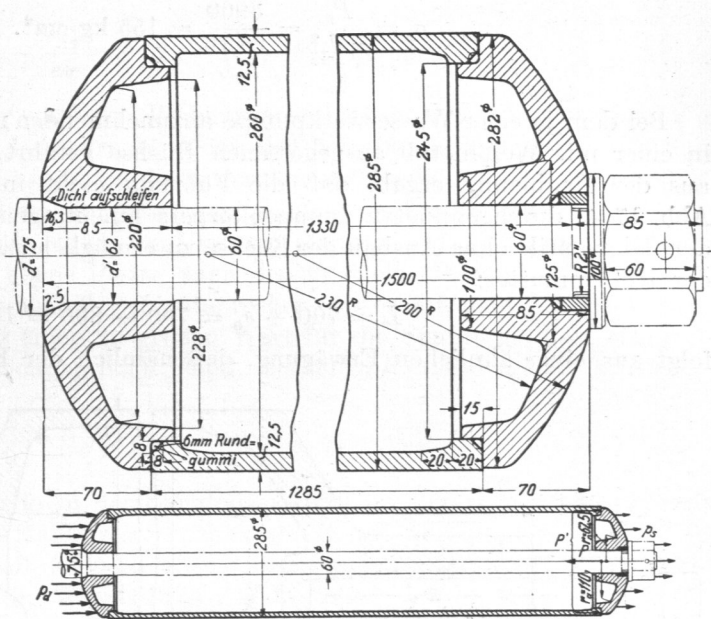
Pumpenkolben zur Wasserwerkmaschine Tafel I.
